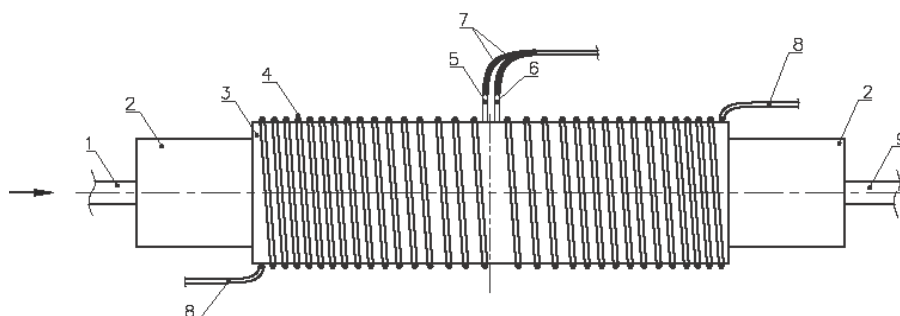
Схема фильтреlementa с нагревателем: 1 и 9 - входной и выходной патрубki, 2 - керамический корпус фильтреlementa, 3 - керамический корпус нагревателя, 4 - нагреватель фехралеый, 5 и 6 - датчики температуры терморегулятора и сигнализатора, 7 - выходы датчиков, 8 - выходы нагревателя
